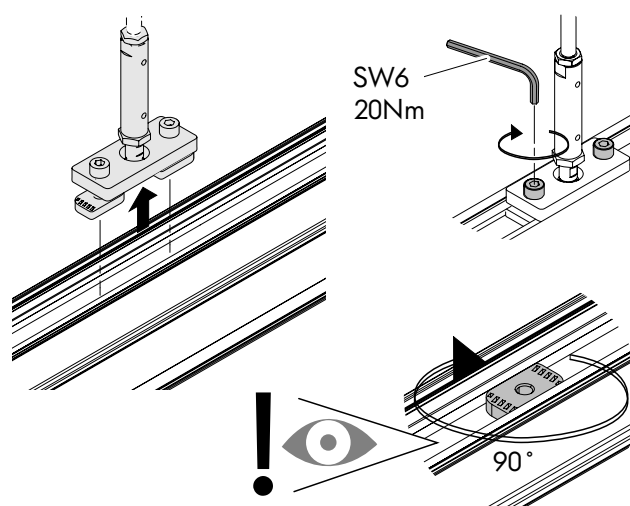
Montaje del perfil en la suspensión pendular del techo
